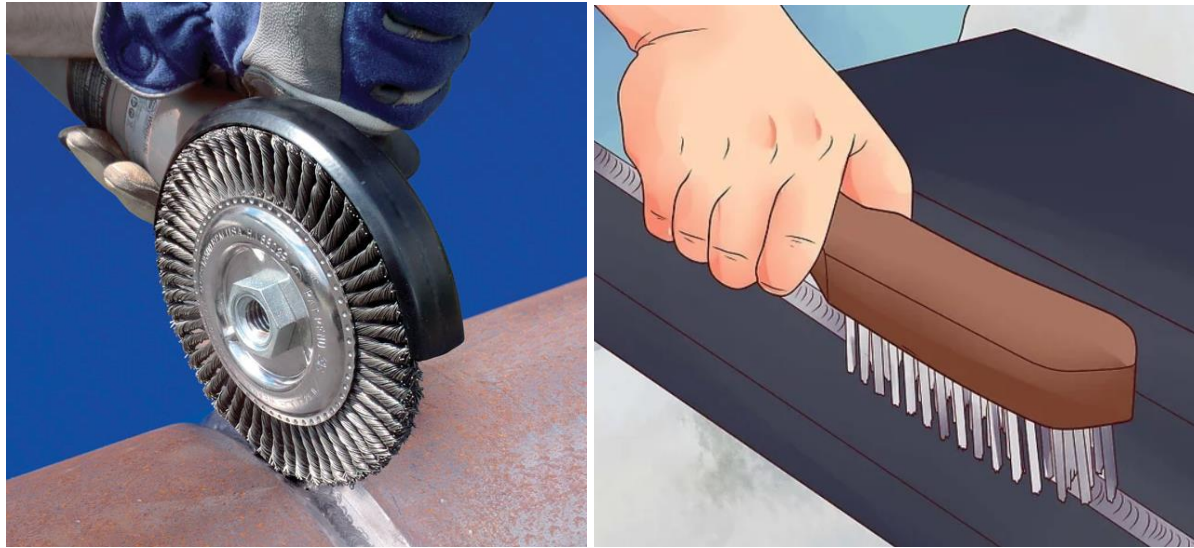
Limpieza mecánica de juntas a soldar y de las juntas soldadas
